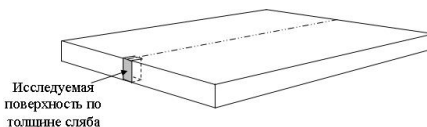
Схема отбора темплетов из слывовой непрерывнолитой заготовки
